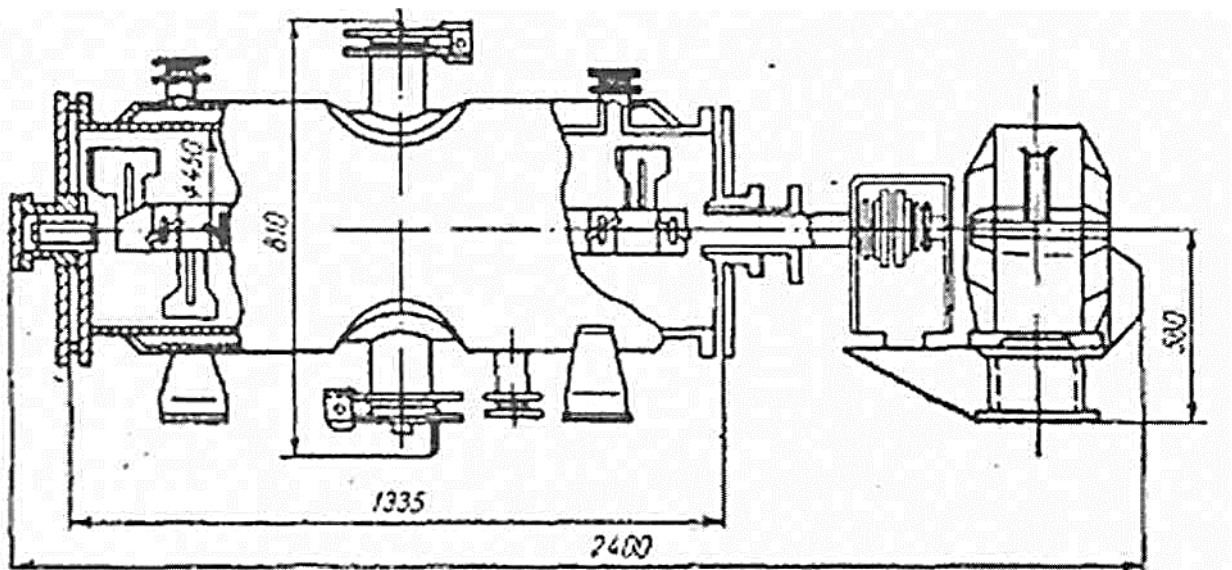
Вакуумна циліндрична сушарка з реверсивною мішалкою
